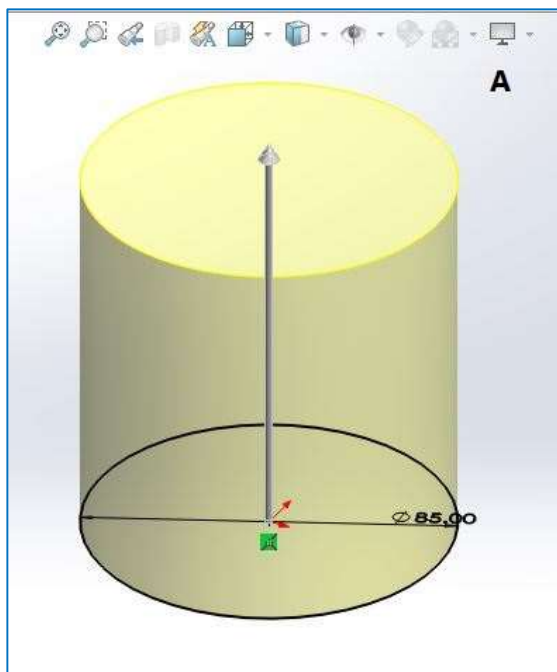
A.B : *Étape de la construction d'une forme 3D du piston
